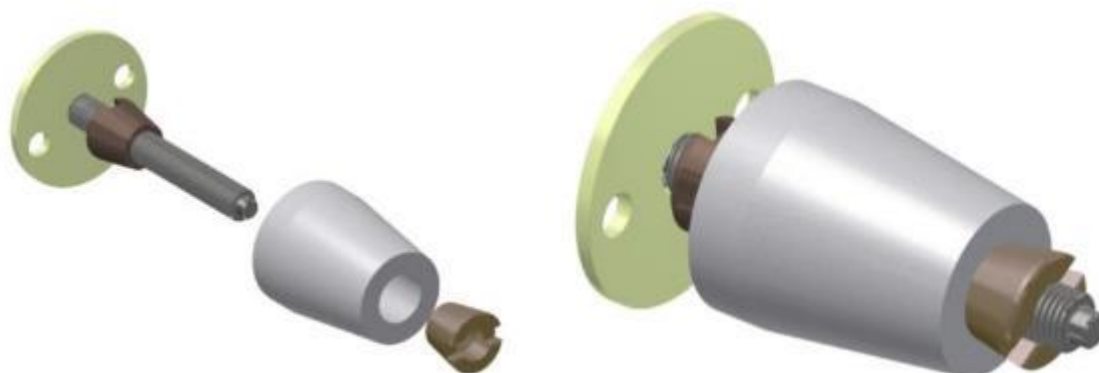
Die Montage des Blocks im Einbettwerkzeug.
